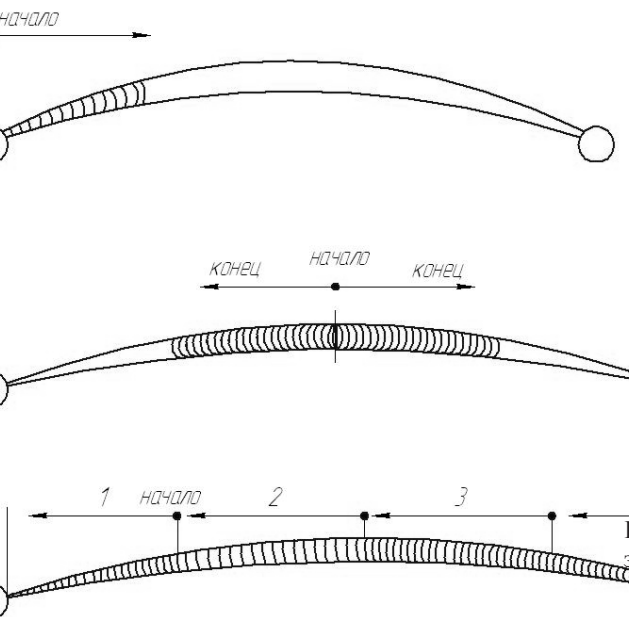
Схемы заварки короткой, средней и длинной трещины
